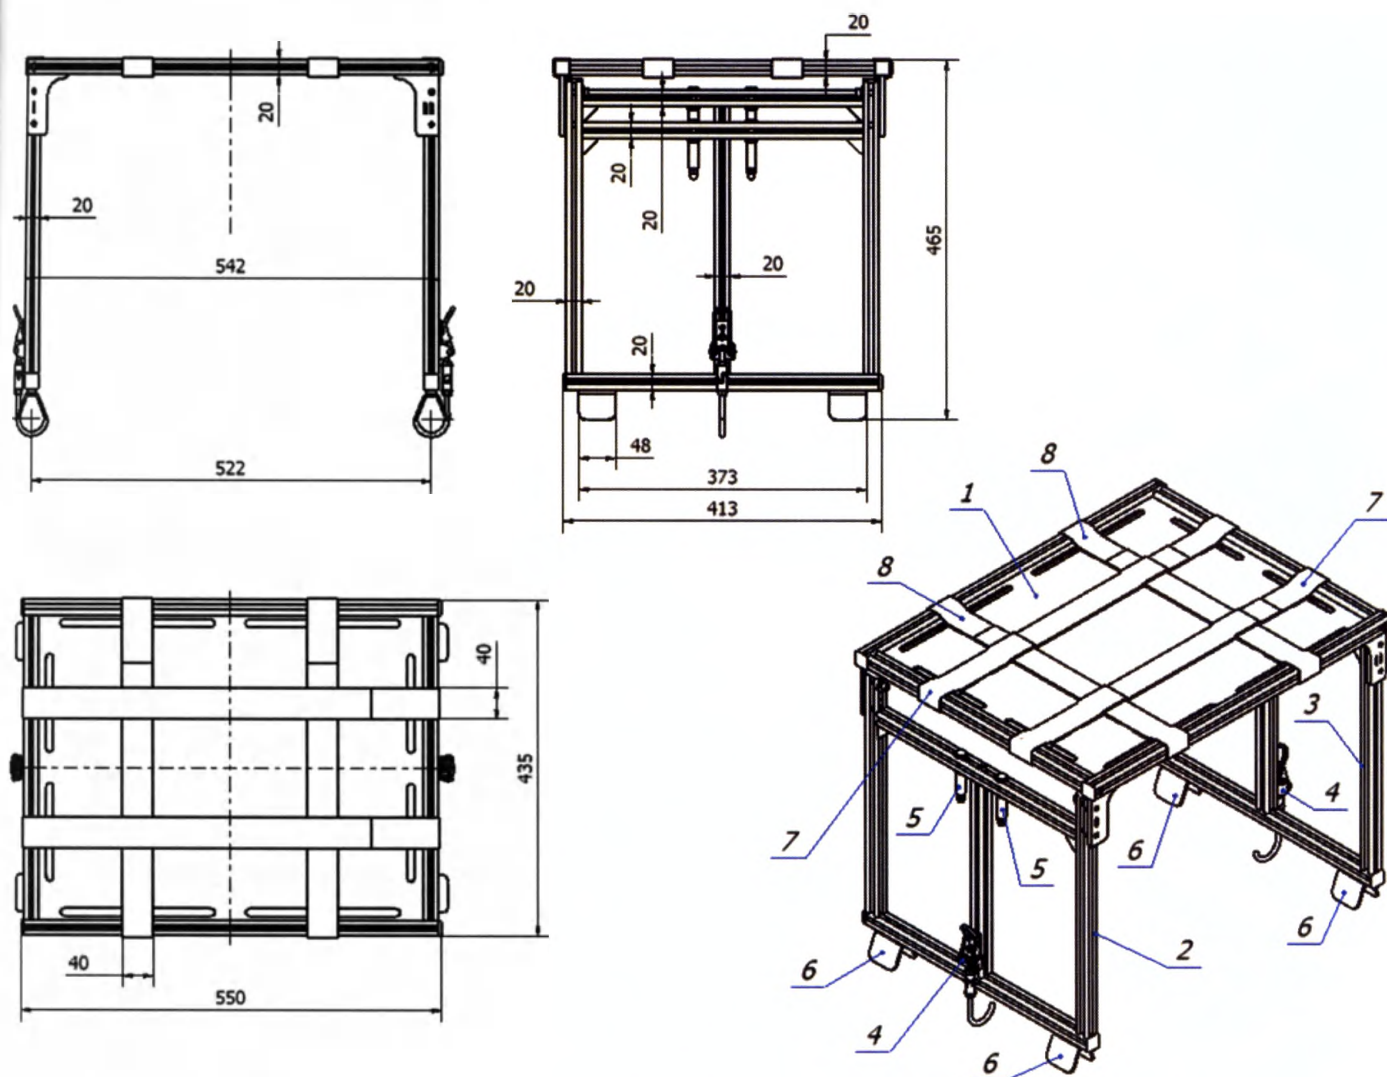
Общий вид полки для оборудования (в рабочем положении)
